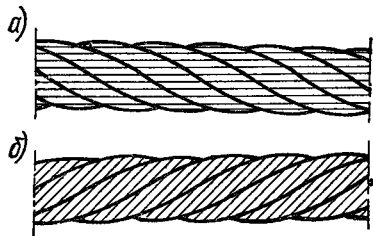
Сочетание направлений свивки в канатах двойной свивки: а — крестовая свивка; б — односторонняя
